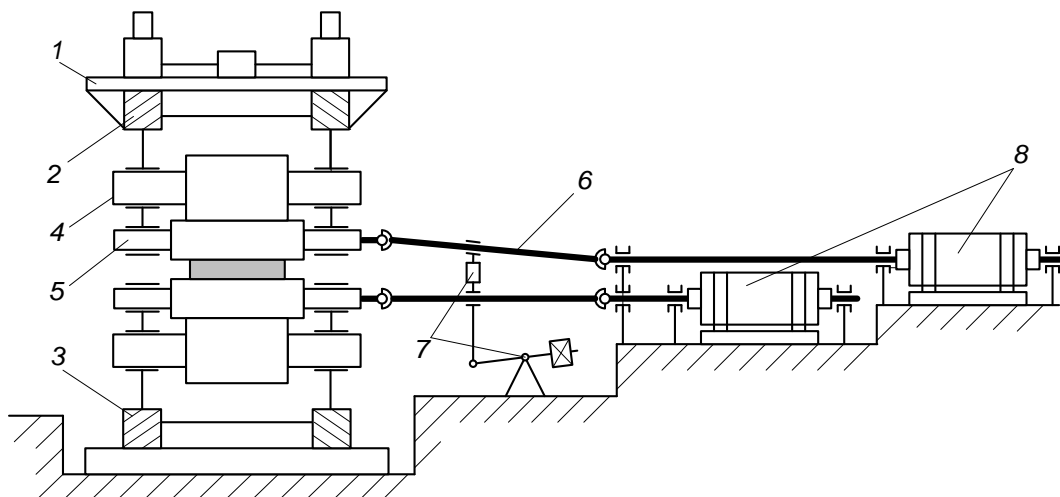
Кинематическая схема реверсивной клетки стана 5000: 1 – станина; 2 – электромеханическое НУ; 3 – гидравлическое НУ; 4 – опорные валки; 5 – рабочие валки; 6 – выдвигаемые шпиндели; 7 – уравнивающее устройство; 8 – двигатели
